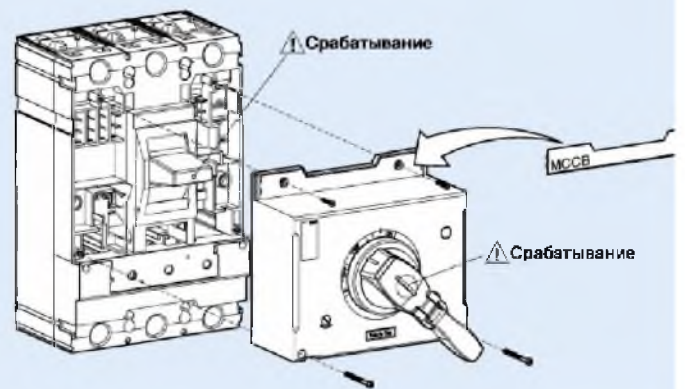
Габаритные и установочные размеры, способ установки стандартной поворотной рукоятки TS800
